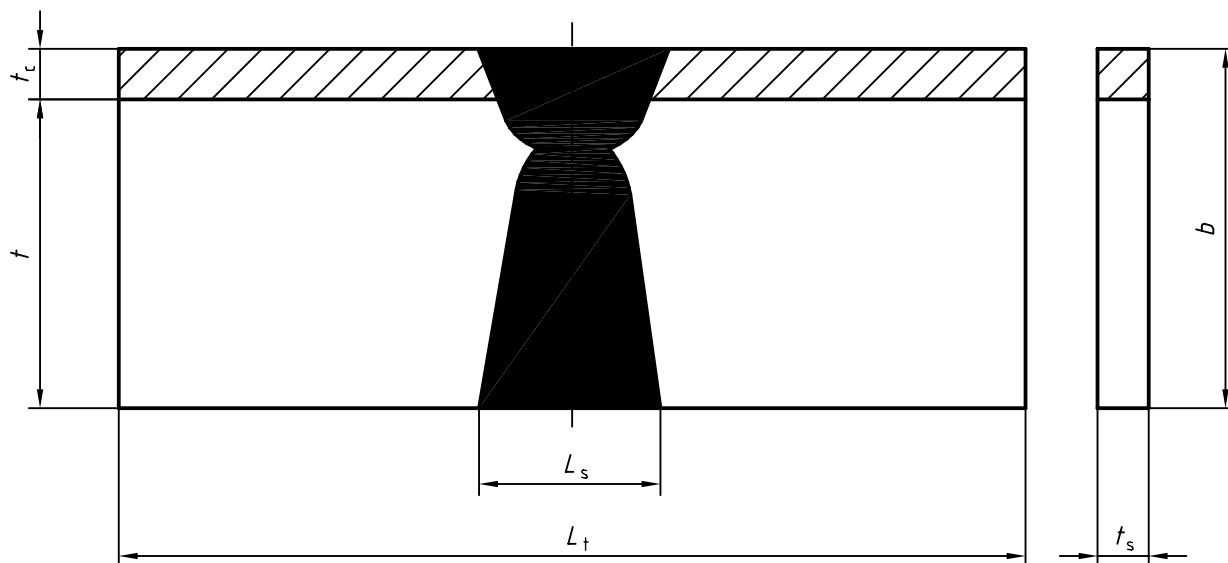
Éprouvette de pliage endroit sur revêtement avec soudure bout à bout (FBCB)
